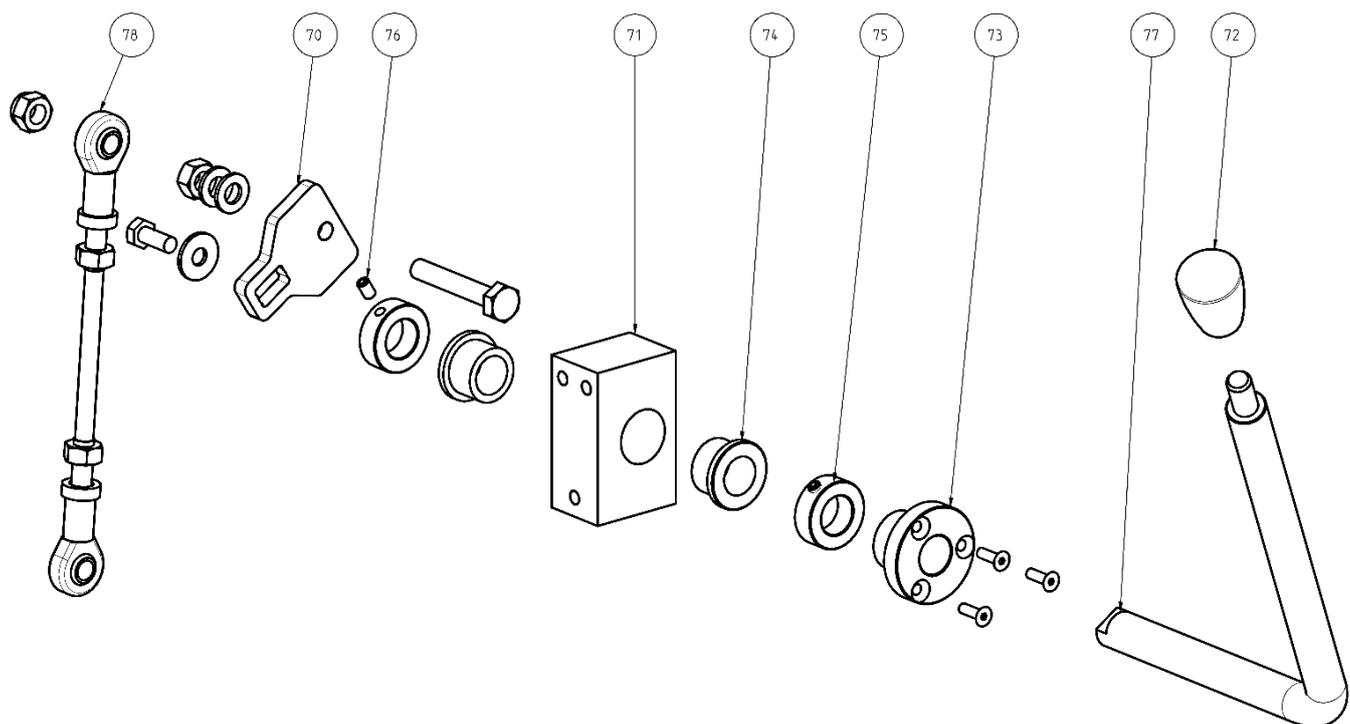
Gruppo sollevamento / Lifting assembly
